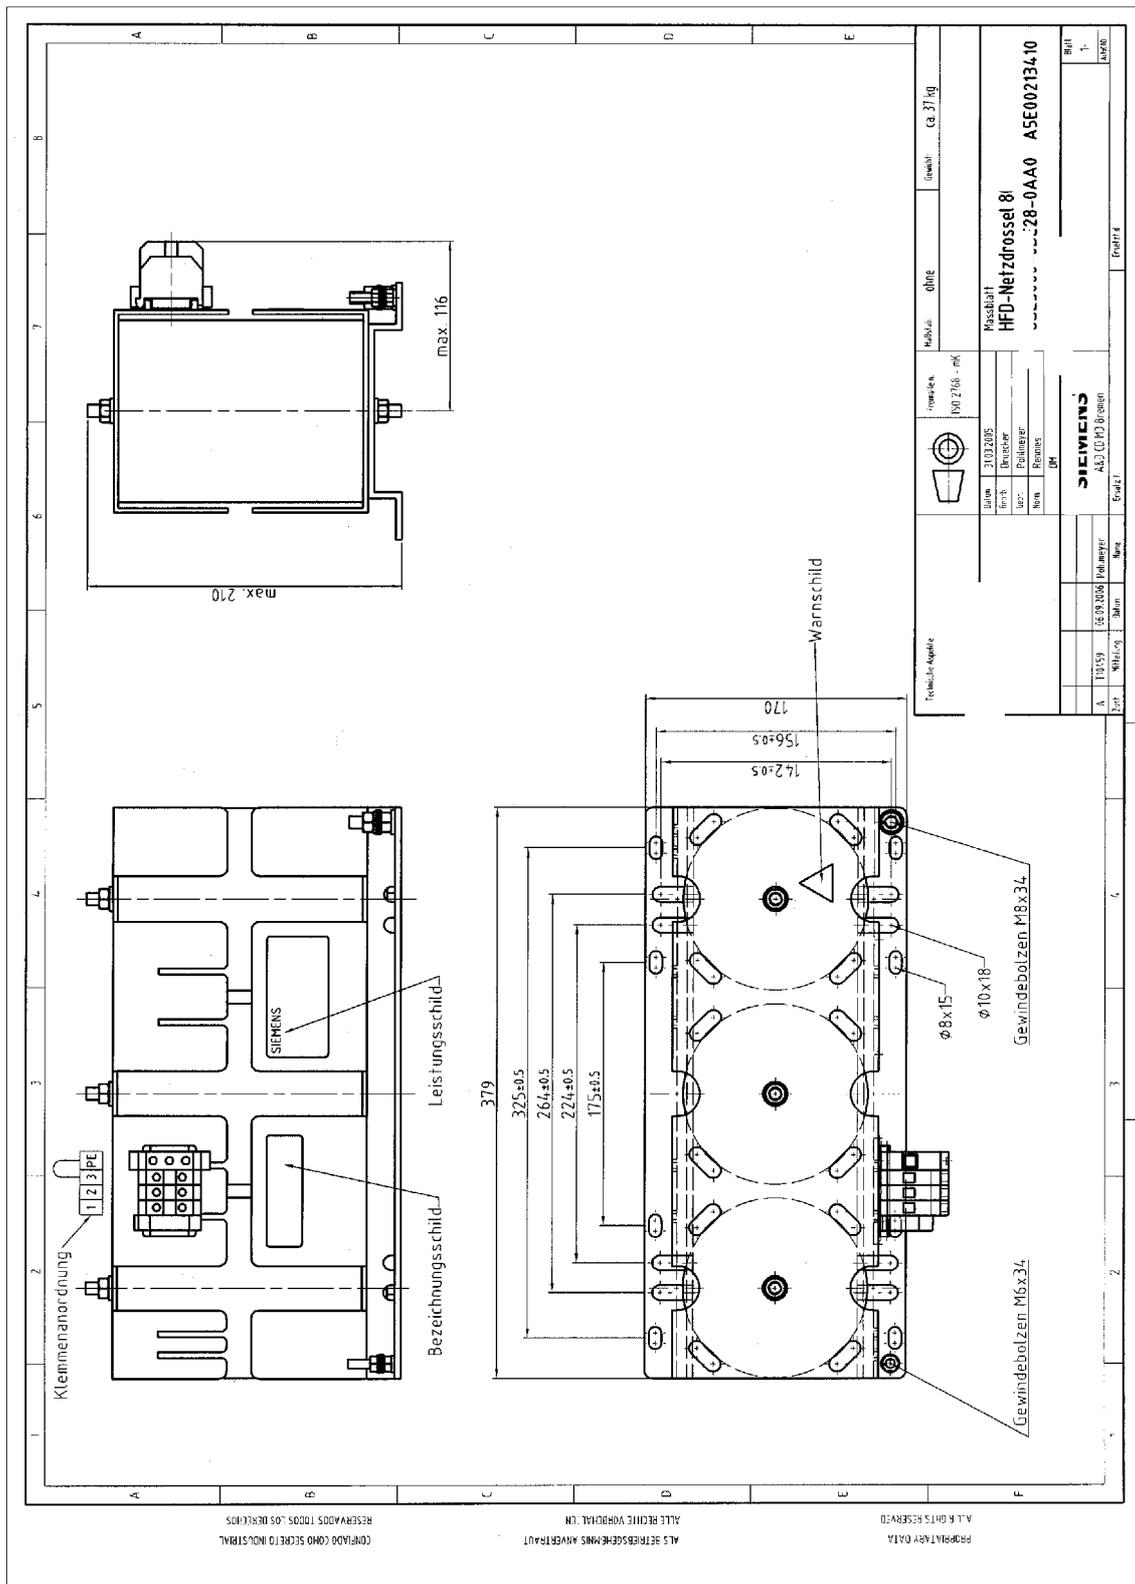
Bobina HFD trifase/bobina di commutazione 80 kW, 6SL3000-0DE28-0AAx
